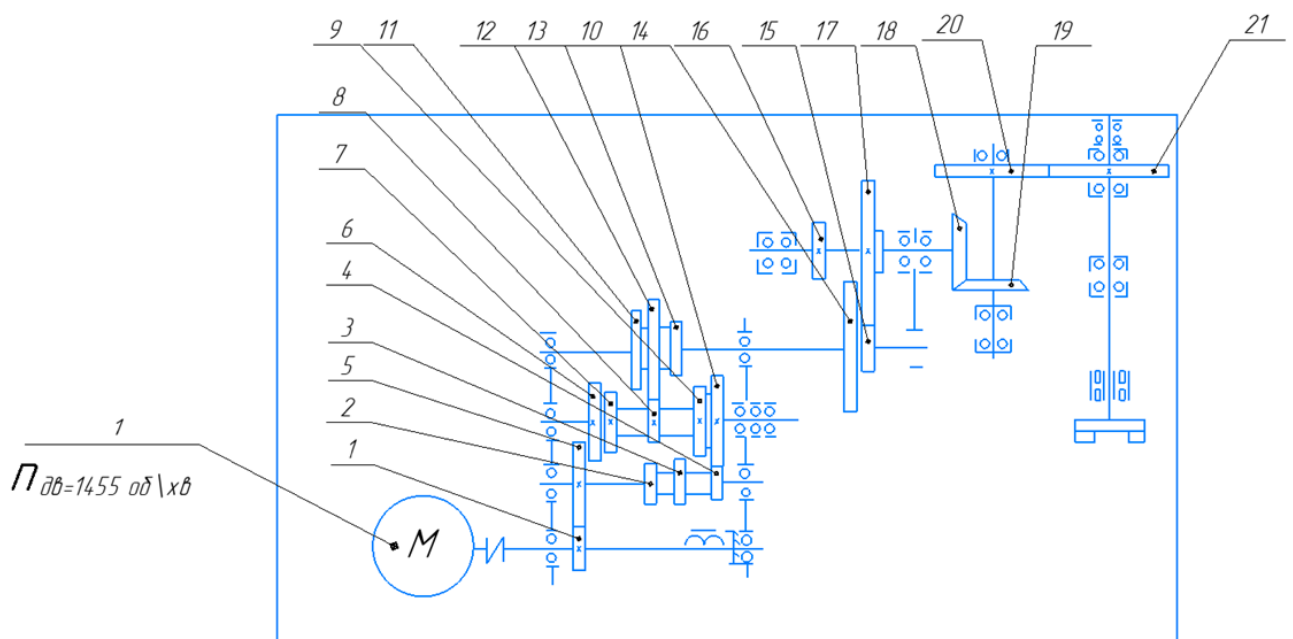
Первісний варіант кінематичної схеми верстата 16K20Ф3С32
